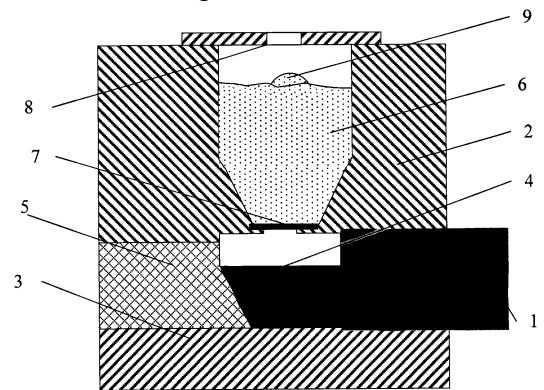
Принципова схема металургійного зварювання: 1 – основа різця; 2 – верхня напівформа; 3 – нижня напівформа; 4 – місце зварювання; 5 – вогнестійкий матеріал; 6 – екзотермічна суміш (у насипному виді); 7 – титанова пластина (товщиною 0,5 мм); 8 – кришка з отвором у центрі для виходу газів; 9 – титановий запал
